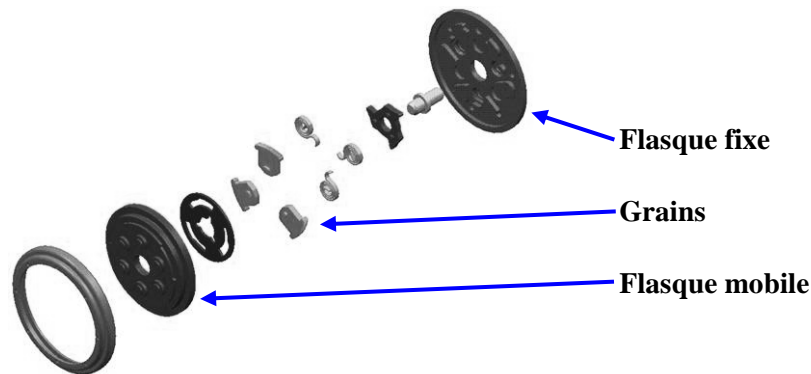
Mécanisme d'articulation discontinue : ensembles des pièces.
